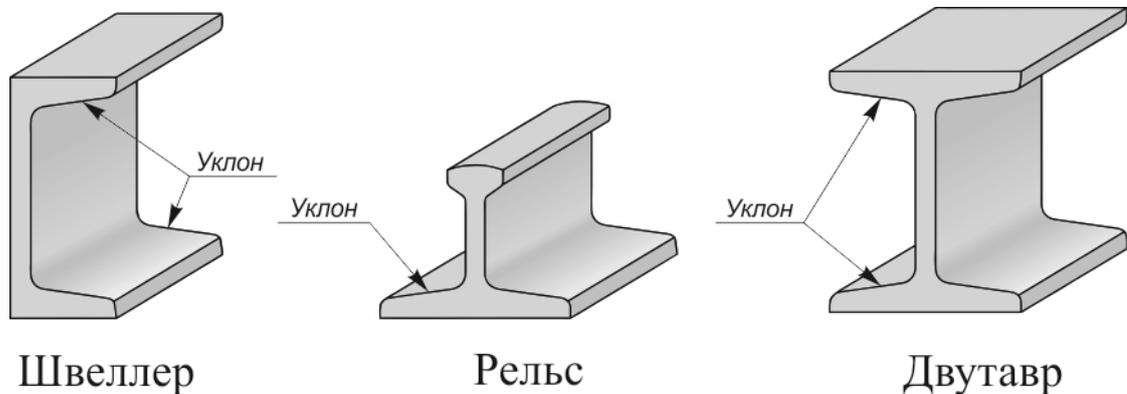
Стальной фасонный прокат для металлоконструкций
